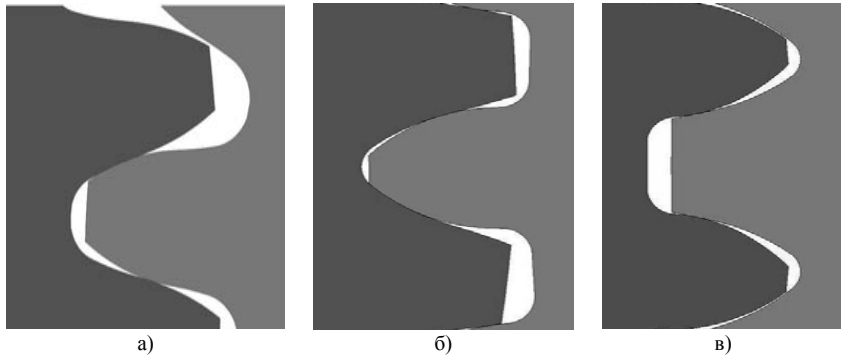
Профили боковых поверхностей шестерни и колеса:
